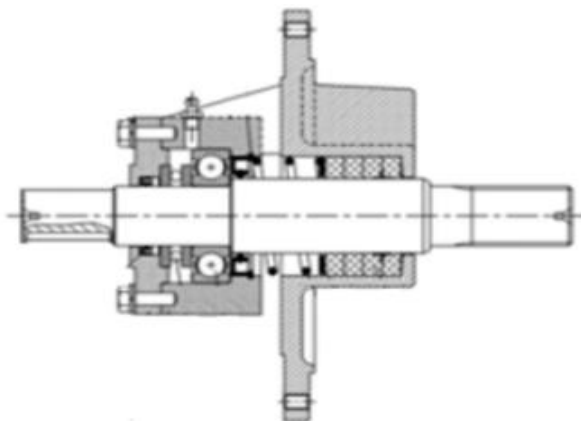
Схема підшипникового вузла та ущільнення валу шнека
